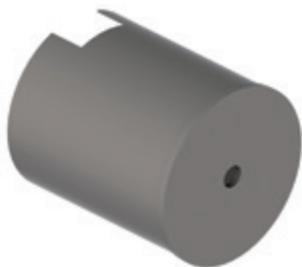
Dispositivo de bloqueo del eje para motores con cojinete de rodamiento.
